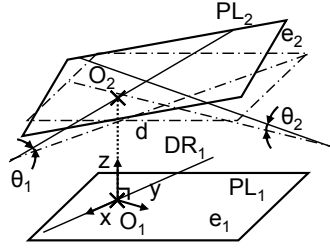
Construction du repère à partir de deux plans parallèles
